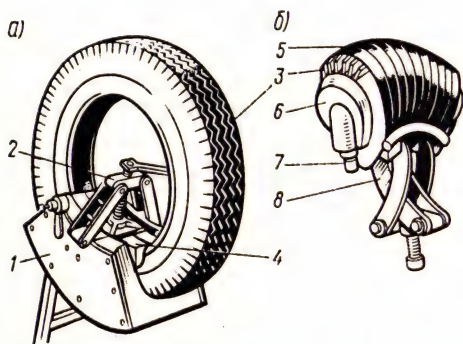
Аппараты для вулканизации покрышек: а — мультя; б — сектор; 1 — корпус; 2 — прижимное устройство; 3 — покрышка; 4 — бортовые накладки; 5 — корсет; 6 — паровая камера; 7 — штуцер для подвода пара; 8 — устройство для затяжки корсета
